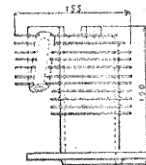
Cylindre de motocyclette obtenu par moulage à la machine.
